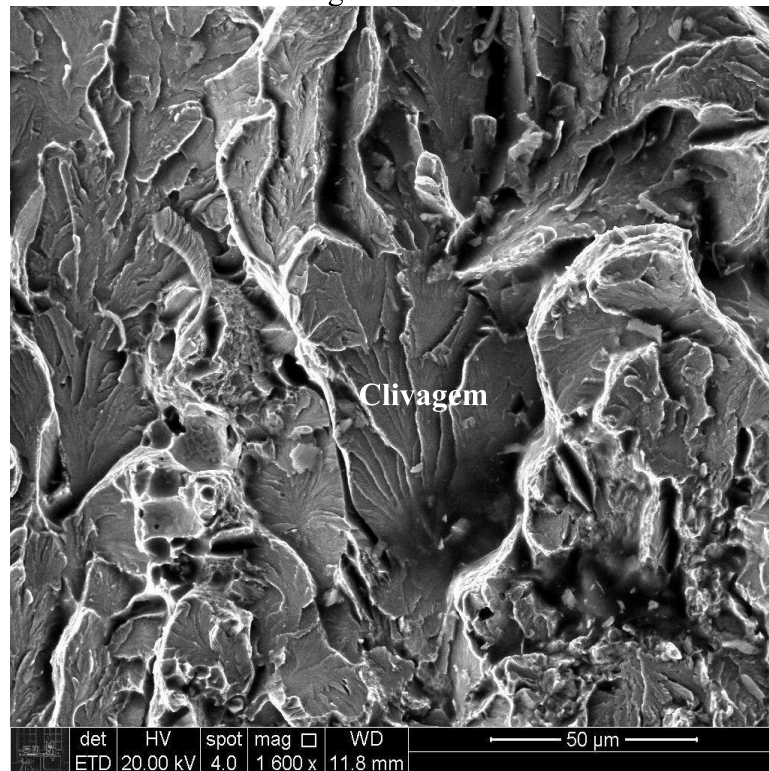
Imagem obtida por MEV da superfície de fratura do corpo de prova da solda S16.
